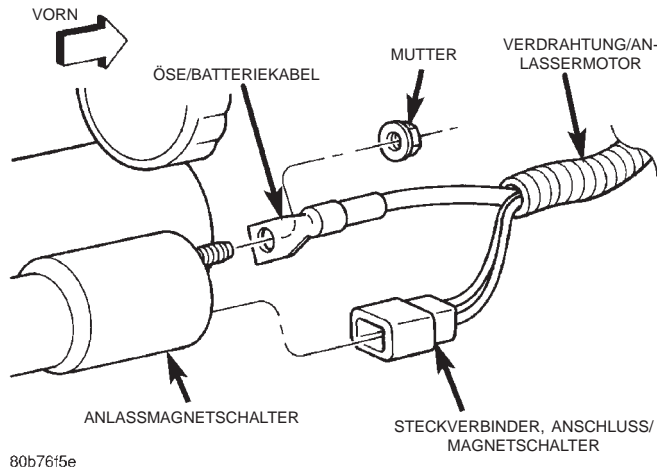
Verdrahtung des Anlassermotors abklemmen und anschließen—4.0L-Motor
